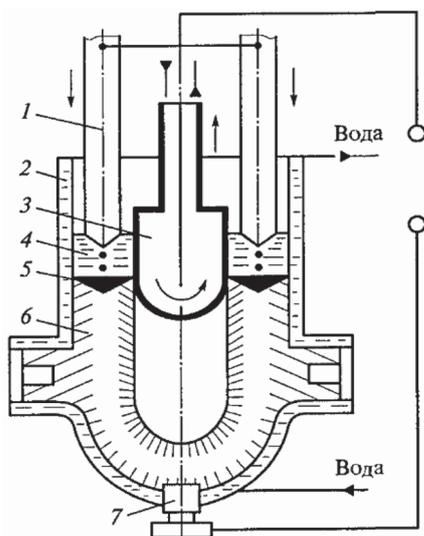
Схема установки электрошлакового литья: 1 – электрод; 2 – металлическая форма; 3 – стержень; 4 – шлаковая ванна; 5 – расплав; 6 – отливка; 7 – затравка
